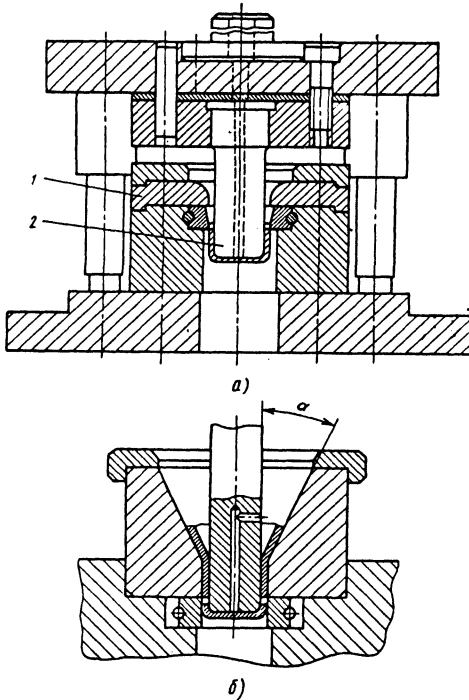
Схемы штампов для вытяжки цилиндрических деталей без применения прижима-складкодержателя
